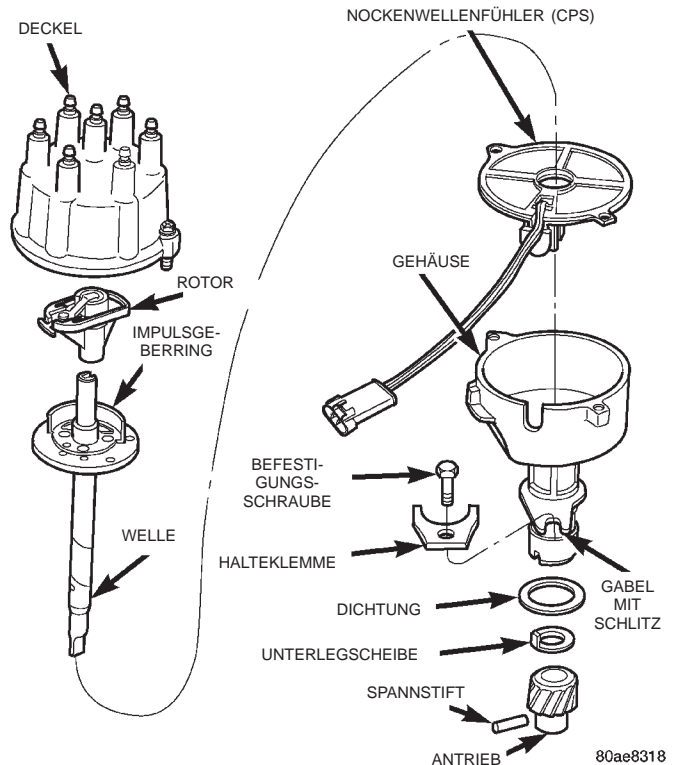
Zündverteiler—2.5L- und 4.0L-Motor
